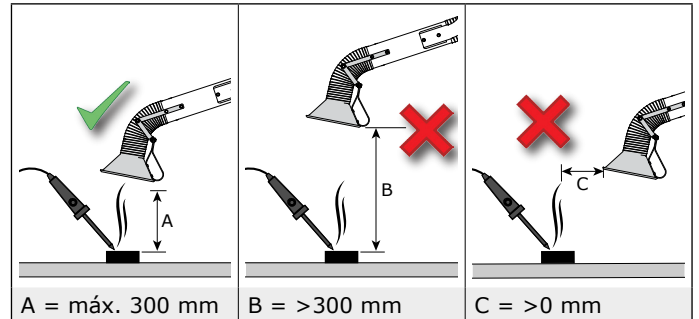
A = posición correcta de la campana (ejemplo: soldadura)
